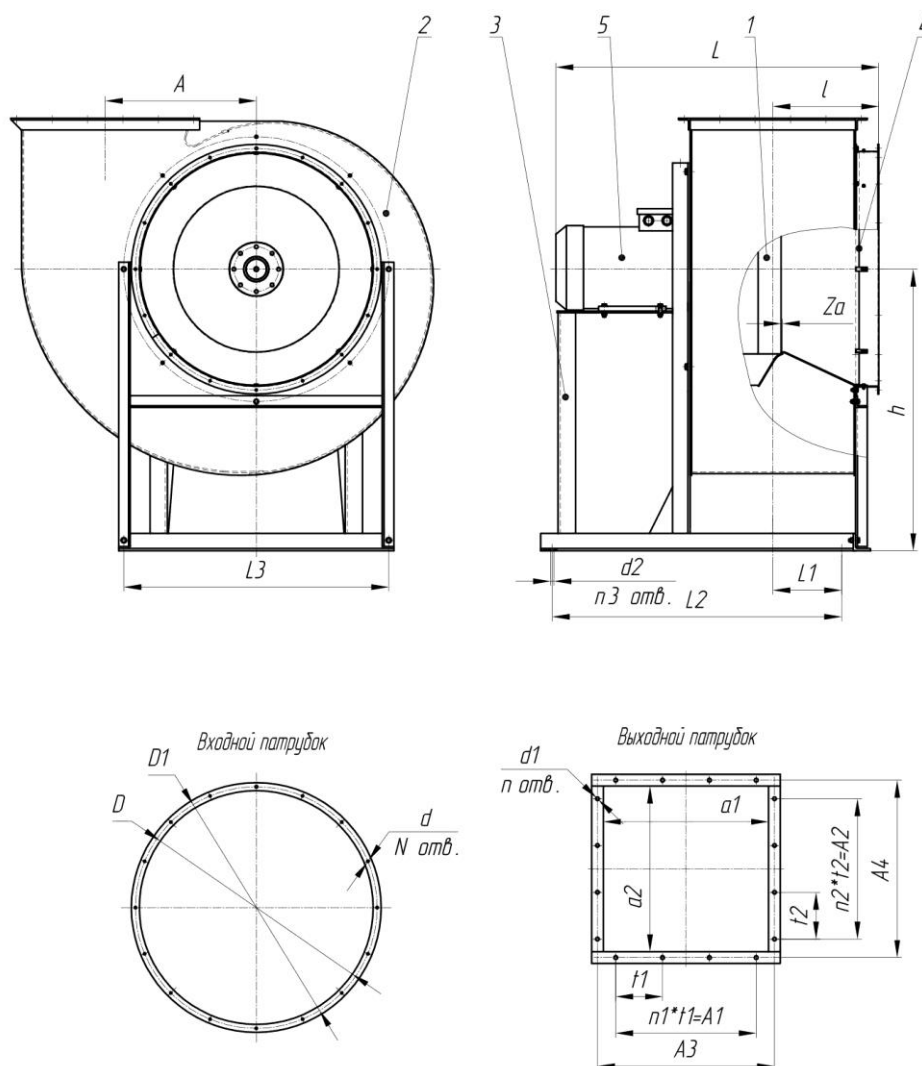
Габаритные и присоединительные размеры ВЦ 4-75 исп-1.
